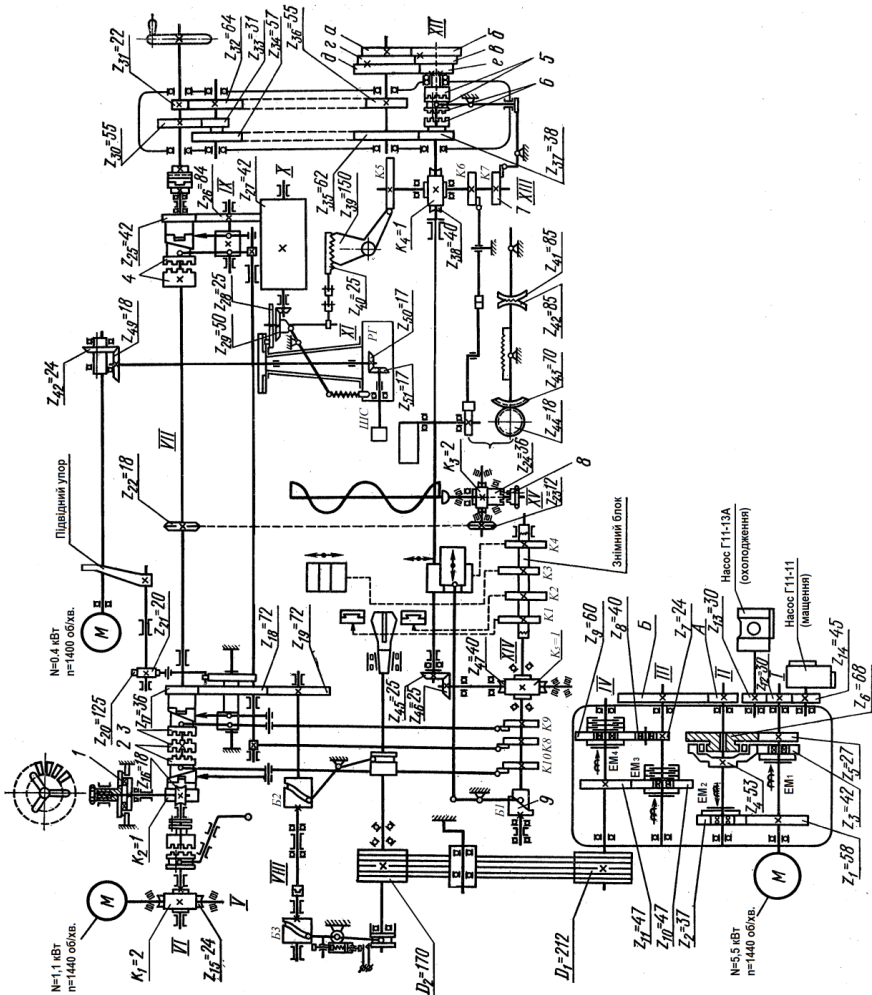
Кінематична схема токарно-револьверного автомата мод. 1Б140
